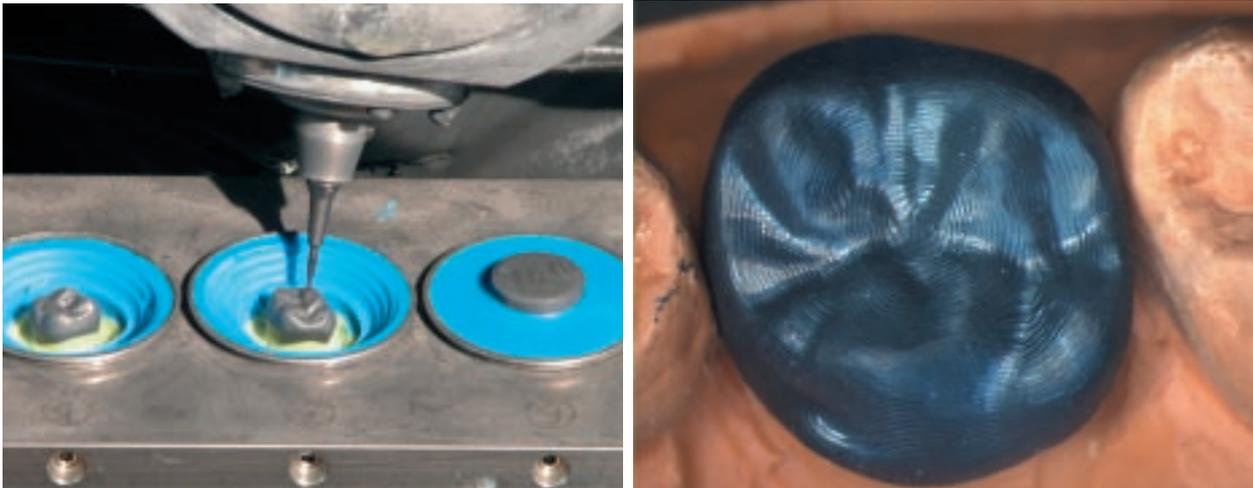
Fräsen einer HPC-Zahnkrone mit dem KaVo Everest® CAD/CAM-System (links) und Blick auf die Kaufläche einer gefrästen HPC-Krone (rechts).
